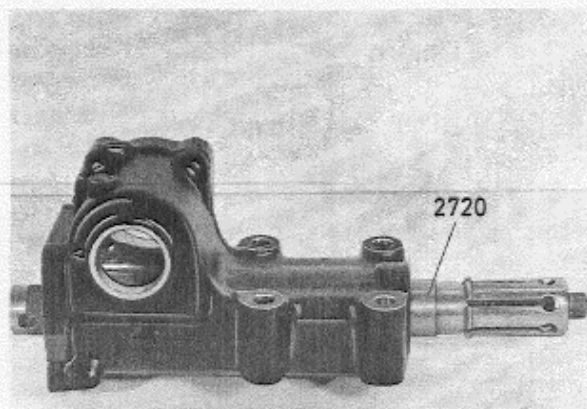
Einschub der Abziehvorrückung mit Expanderhülse
